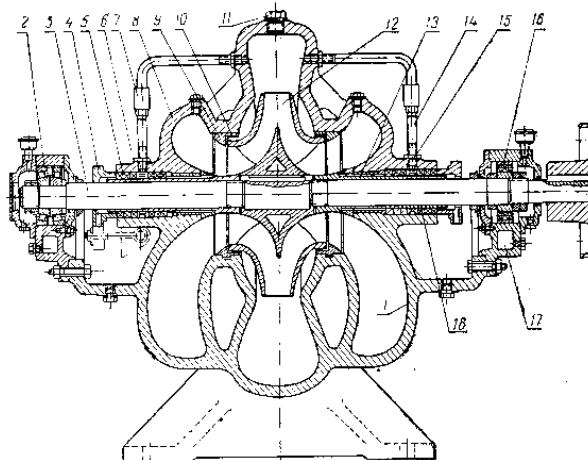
Центробежный одноступенчатый насос Д1250-65 с двухсторонним входом:
